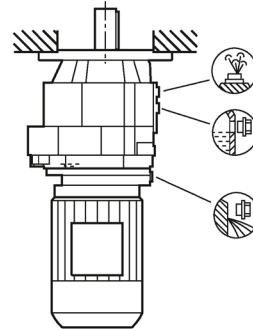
Einbaulagen für Stirnradgetriebe DF/ZF Flanschausführung und DZ/ZZ mit Gehäuseflansch, Baugröße 39
